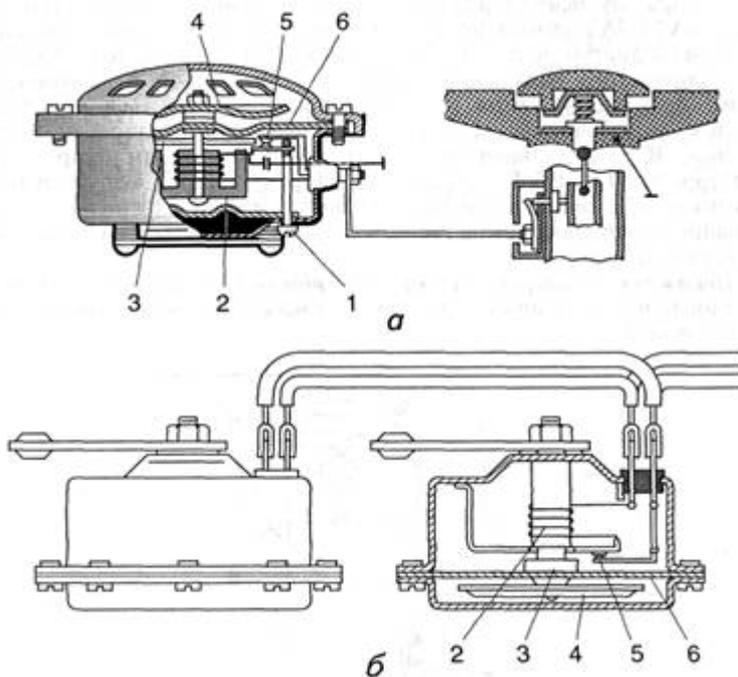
Звуковий сигнал — вібраційного типу без рупорний
